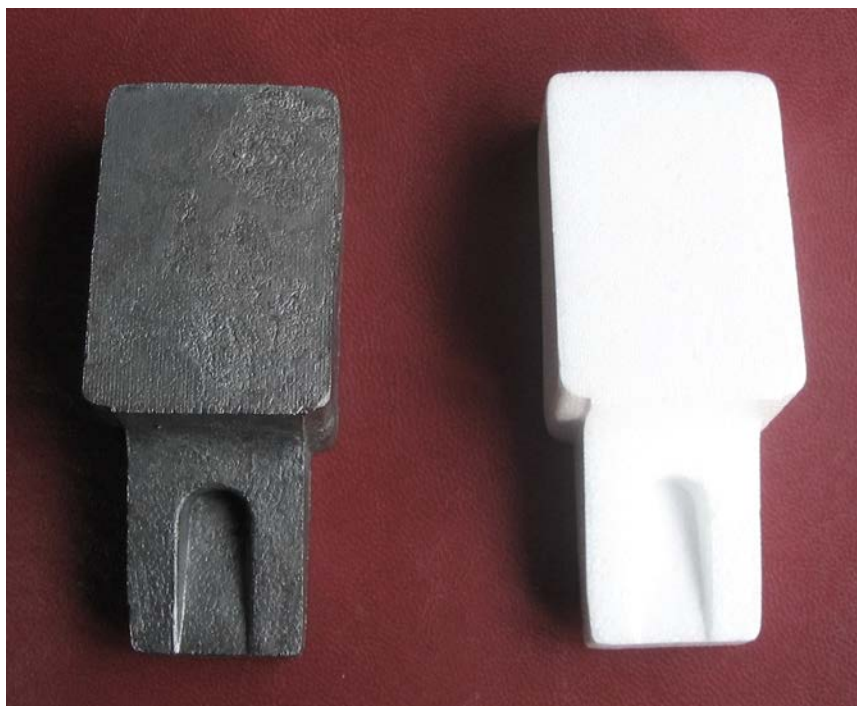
Модель и отливка противовеса из чугуна СЧ20
